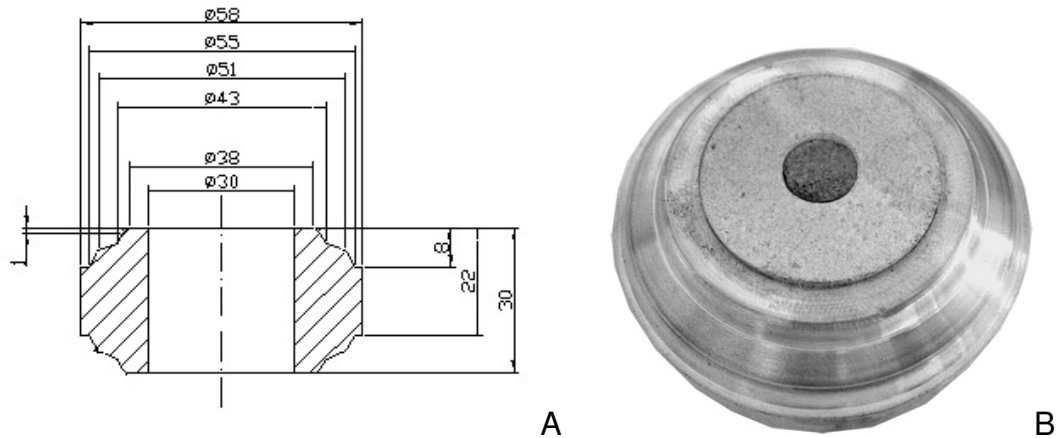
Cápsula de alumínio fabricada para calibração da altura crítica: A – desenho; B – cápsula montada com mistura reativa e tampas.
